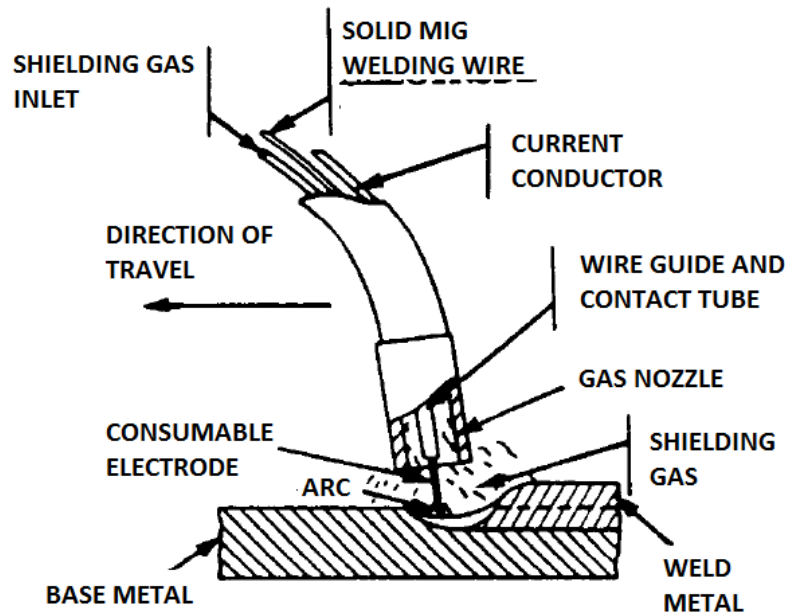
Esquema do processo de soldadura por MIG-MAG [29]
